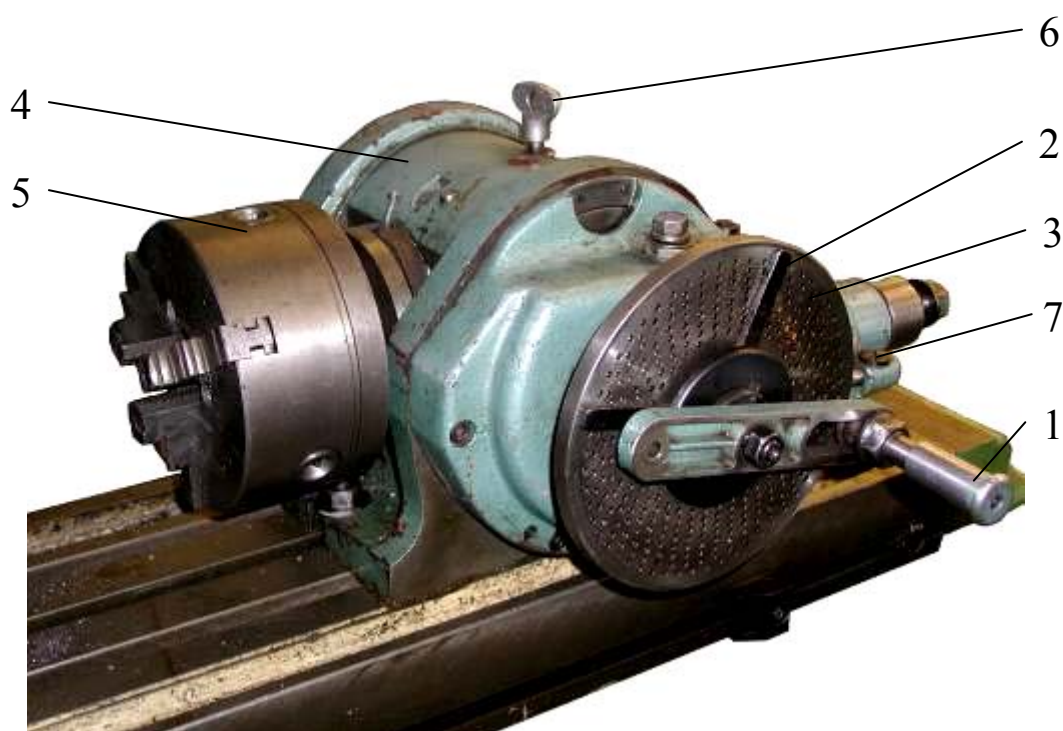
Универсальная делительная головка: 1 – рукоятка с фиксатором; 2 – раздвижной сектор; 3 – делительный диск (лимб); 4 – корпус; 5 – шпиндель с патроном; 6 – фиксатор шпинделя; 7 – фиксатор лимба
